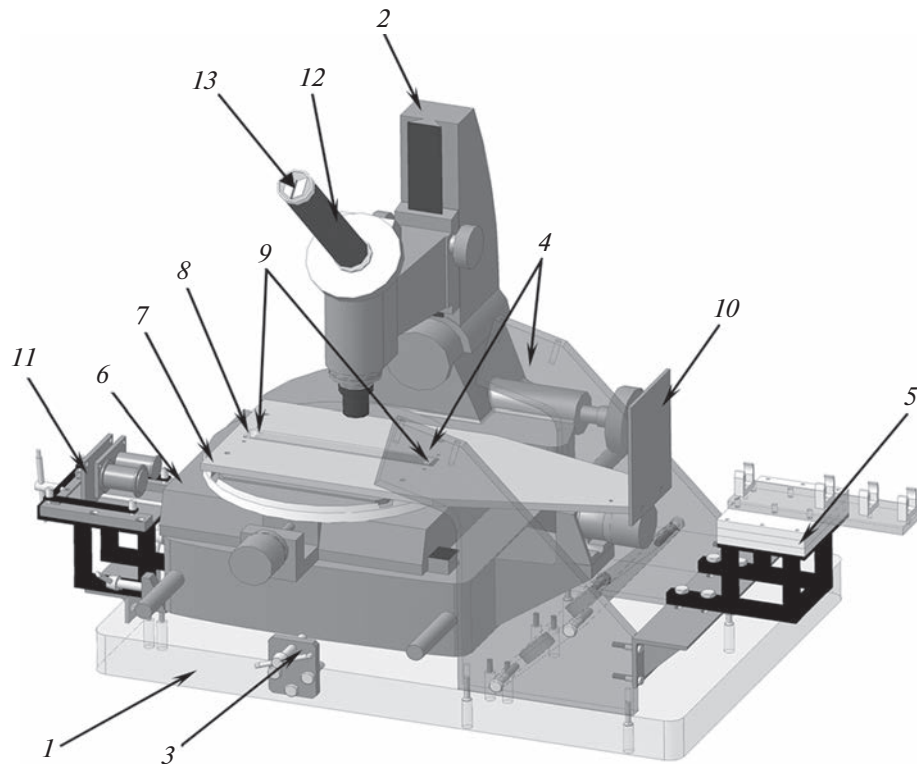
Общий вид стенда “Микроскоп”. 1 – основание; 2 – инструментальный микроскоп БМИ-1; 3 – зажимы; 4 – упоры; 5 – узел крепления облучателя; 6 – подвижный рабочий стол; 7 – опорная плита; 8 – штриховая мера; 9 – накладки; 10 – отражатель; 11 – электромагнитный узел; 12 – коллиматор; 13 – фотоприемник.
